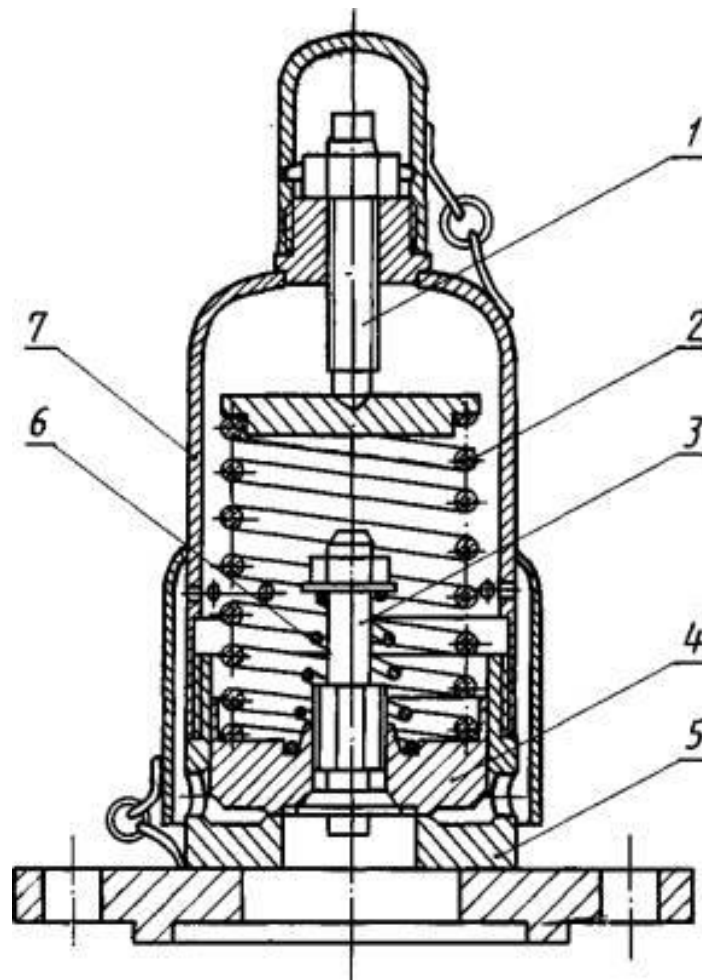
Предохранительно-впускной клапан: 1 – регулировочный винт предохранительного клапана; 2 – пружина предохранительного клапана; 3 – впускной (вакуумный) клапан; 4 – предохранительный клапан; 5 – корпус; 6 – пружина впускного клапана; 7 – колпак
